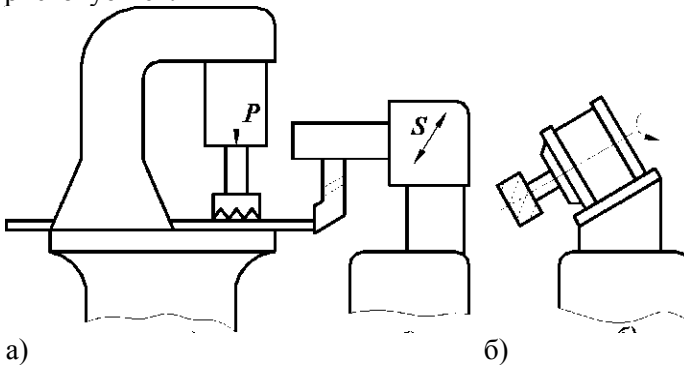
Схема роботи кромкостругального (а) і кромкофрезерного (б) верстатів
